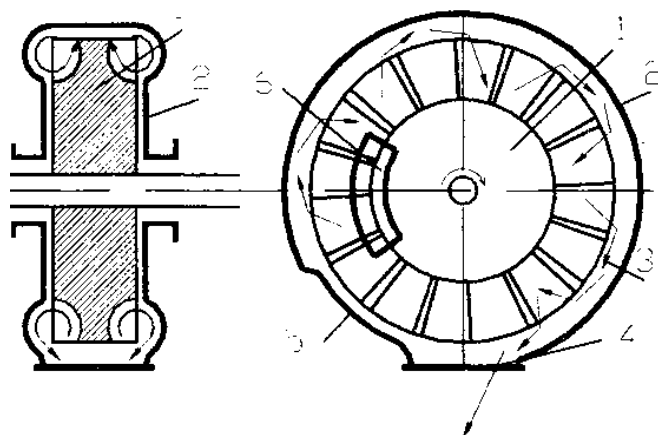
Схема конструкции вихревого насоса: 1 - корпус; 2 - рабочее колесо; 3 - кольцевой канал; 4 - нагнетательный патрубок; 5 - уплотняющий участок; 6 - входное окно
